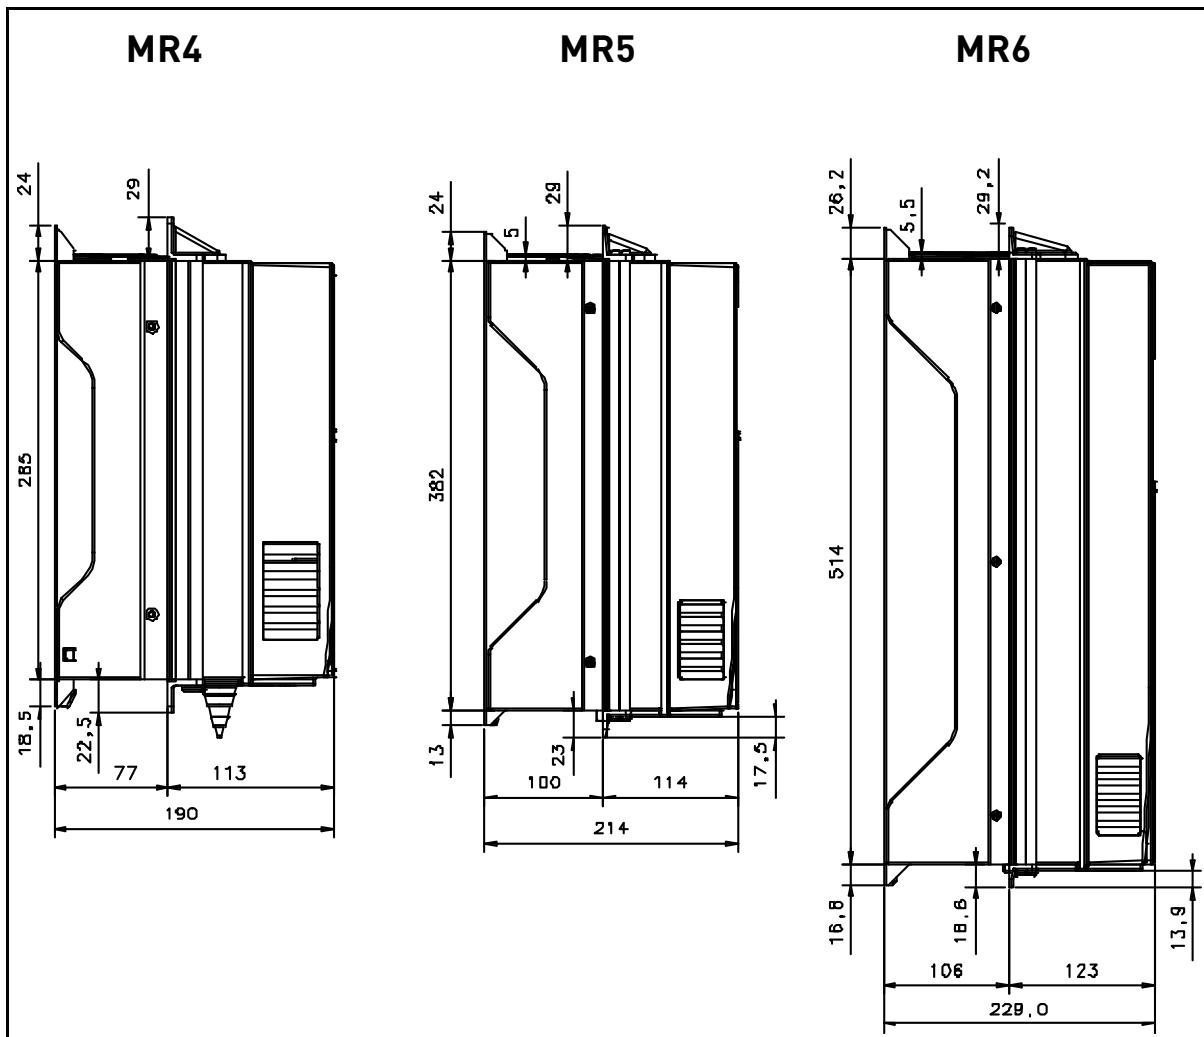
MR4 a MR6, montagem com flange, dimensões de profundidade
